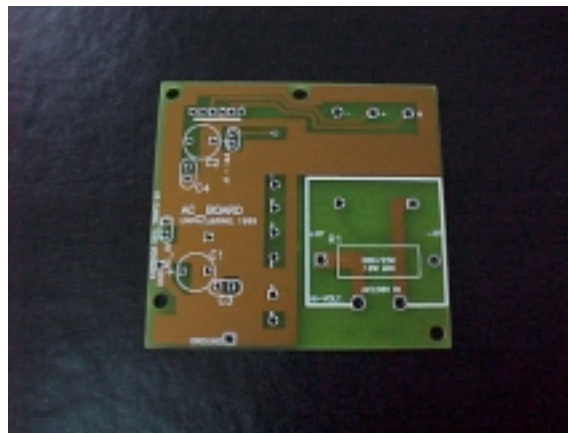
PCB-ACB2 sin componentes soldados.
